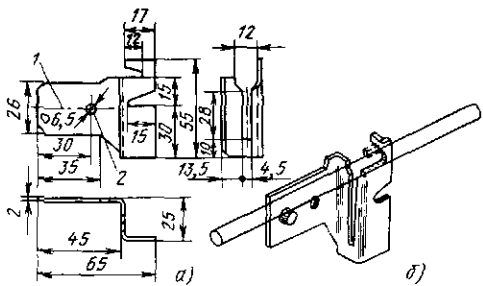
Держатель шиш заземления: 1 - место пристрелки; 2 - отверстие для крепления винтом
